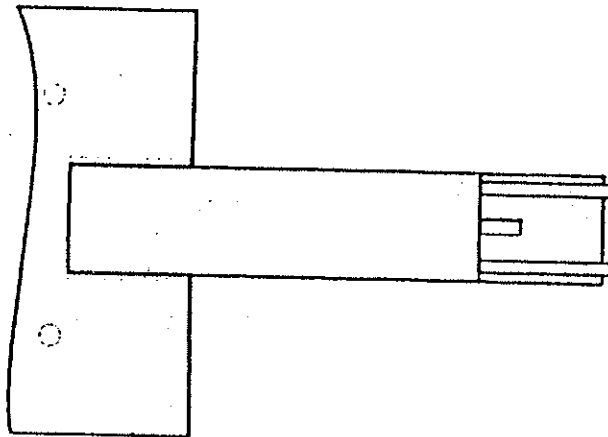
Контроль сварного соединения кронштейна гасителя колебаний со средним листом
